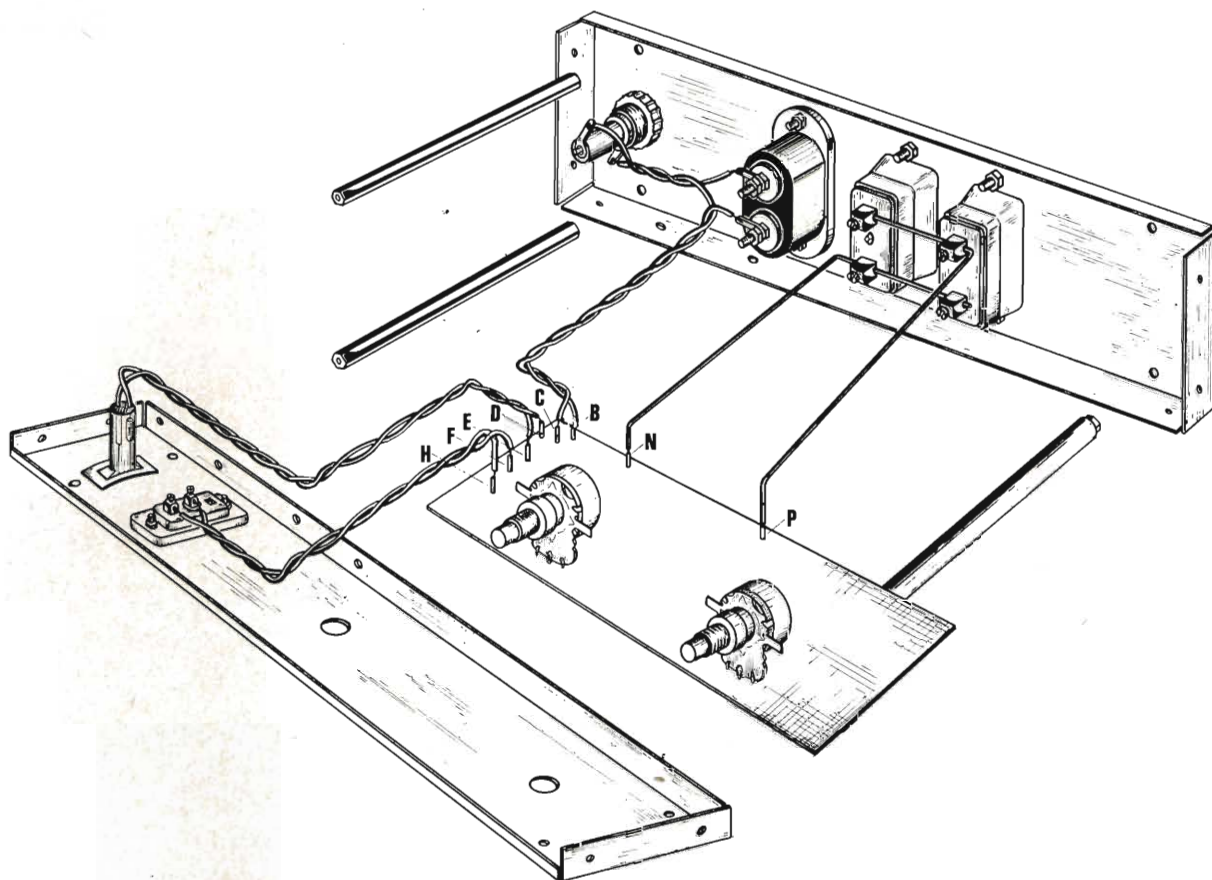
Cablaggio fra circuito stampato e pannelli.
